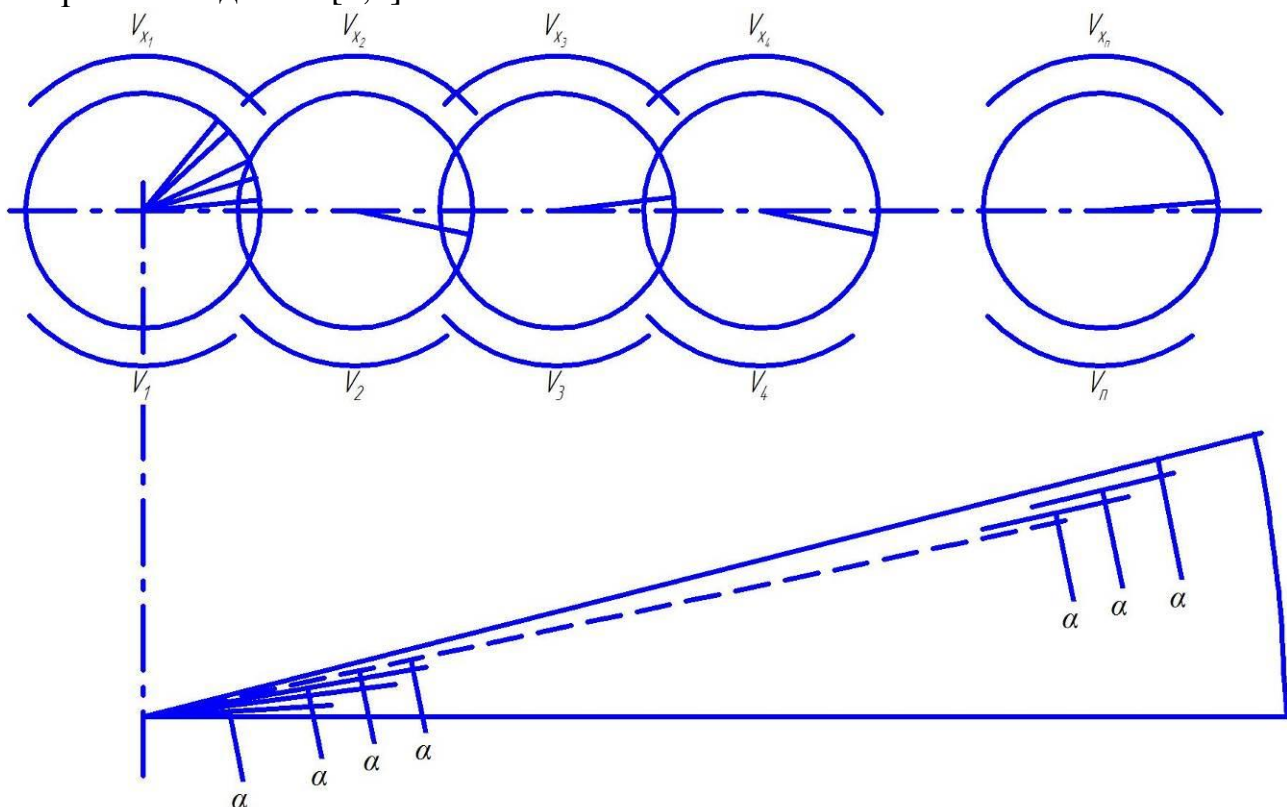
Схема розмірного ланцюга окружного зазору
